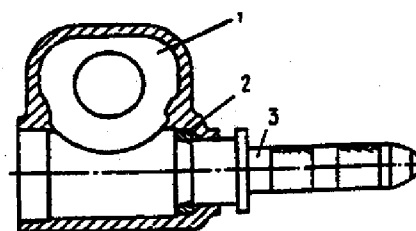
Remoção da pista externa do rolamento superior: 1 - carcaça da caixa da direção; 2 - pista externa do rolamento; 3 - extrator 67.7853-9541.
